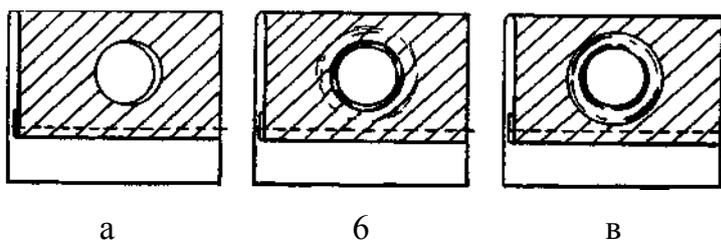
Установка люверсов: а - разметка места расположения колец; б - установка первой части кольца; в - готовое крепление
